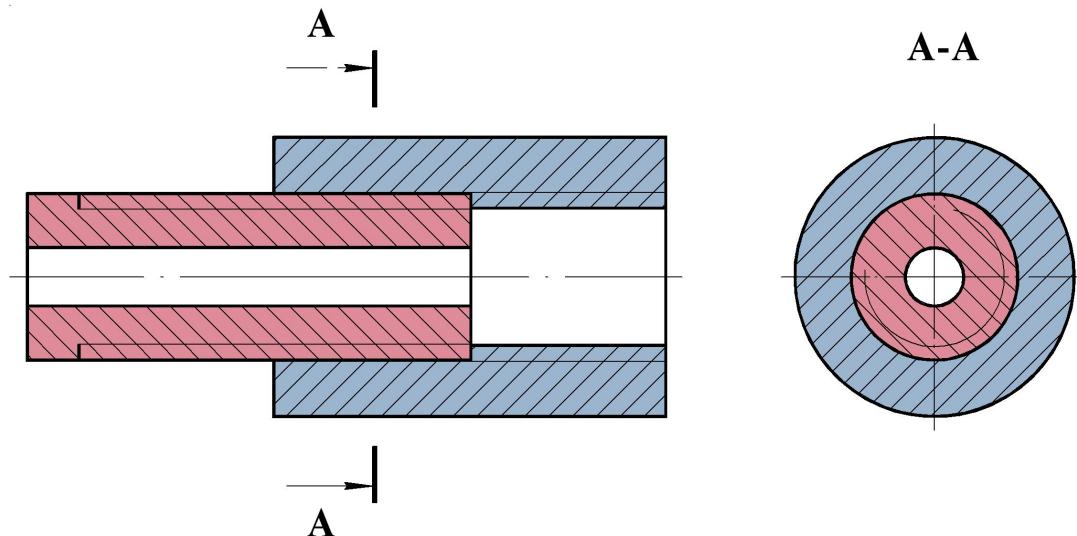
Штриховка деталей резьбового соединения в разрезе
